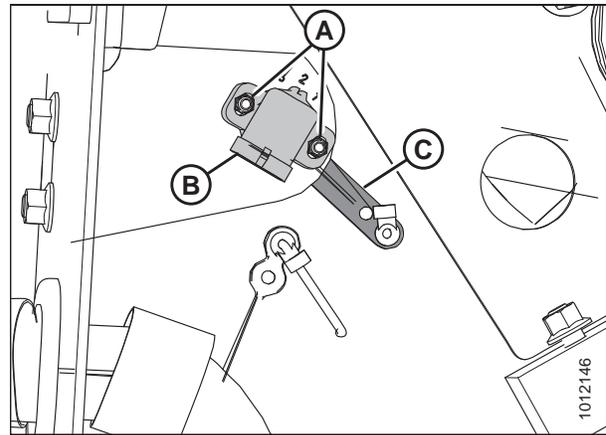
Ensamble del sensor de altura de la plataforma; lado izquierdo
